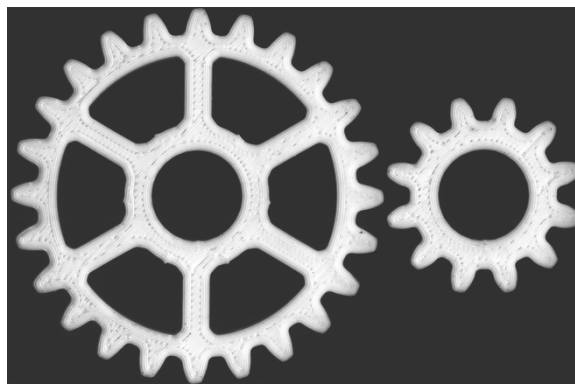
Фотоизображение изготовленной пары зубчатых колес
